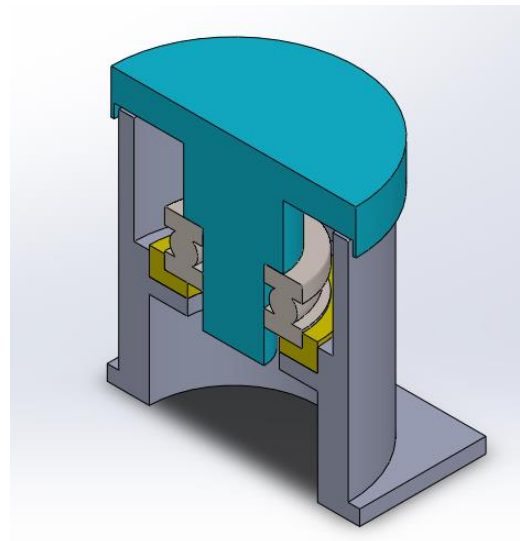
Vista del corte longitudinal del sistema de giro. Fuente: Propia.
